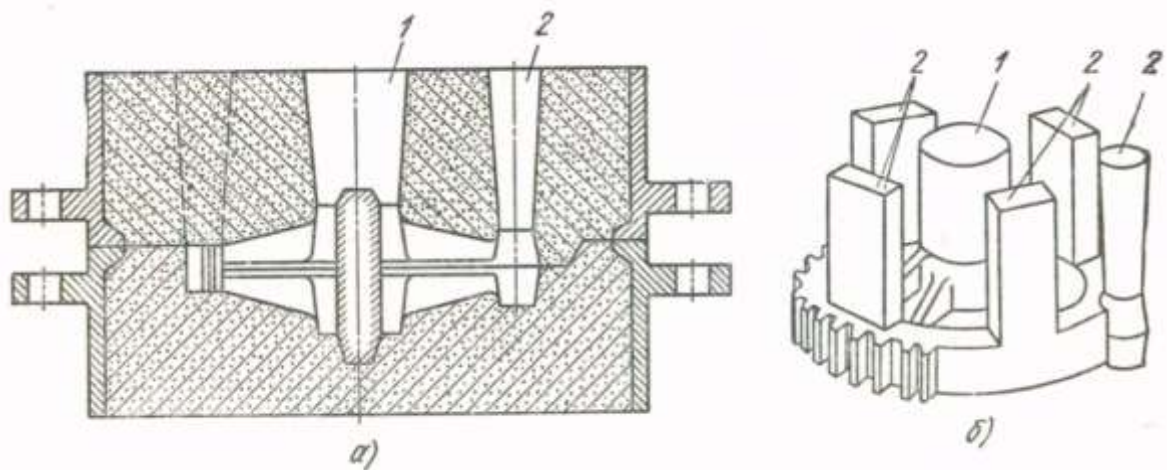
Форма для виливків з вуглецевої сталі:
